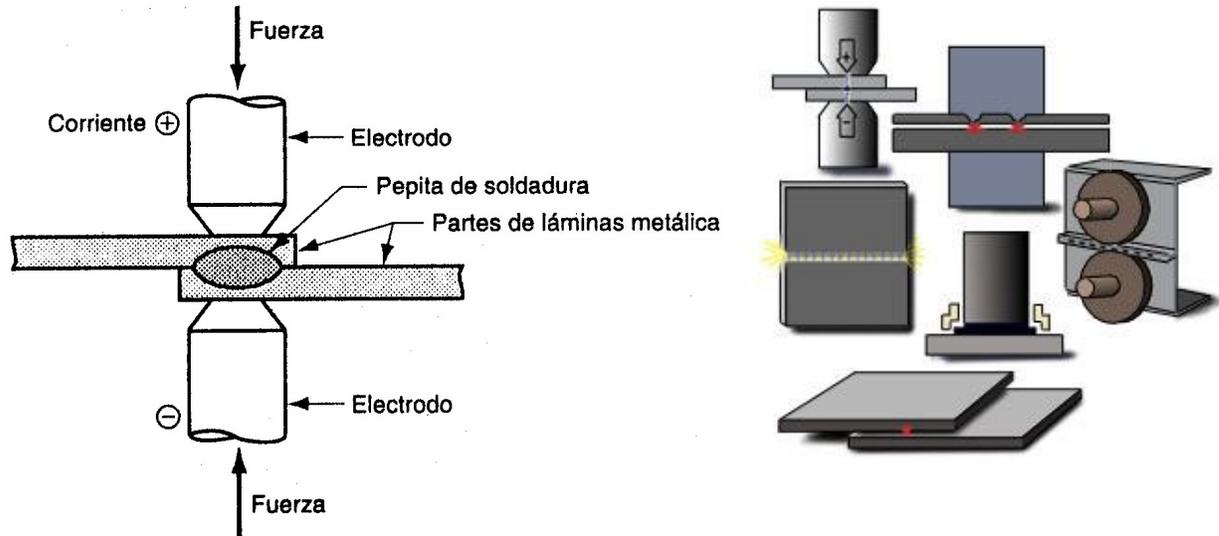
Soldadura por resistencia mostrando los componentes en la soldadura de puntos, el proceso predominante en el grupo de soldadura por resistencia
